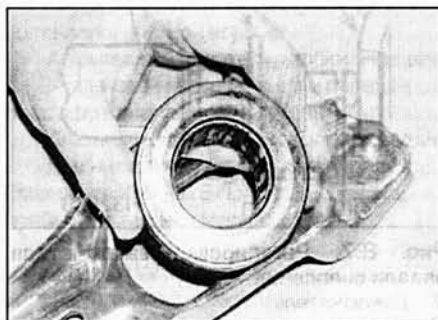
,б. ...отсоедините рычаг от подшипника
